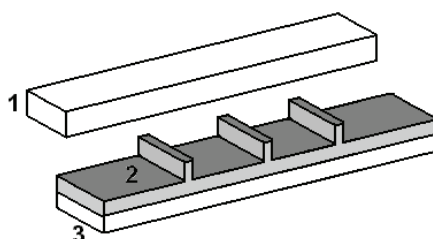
Esquema de montagem do motor de Lim.
